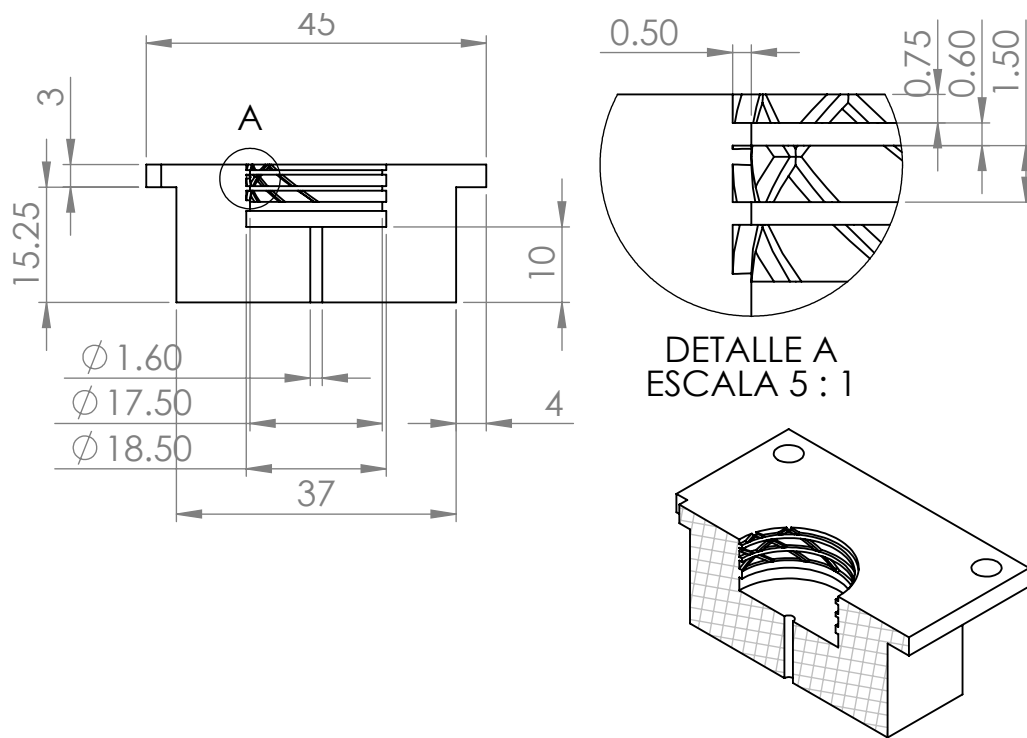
Vista en corte del molde del *Robot Tilt* parte A
